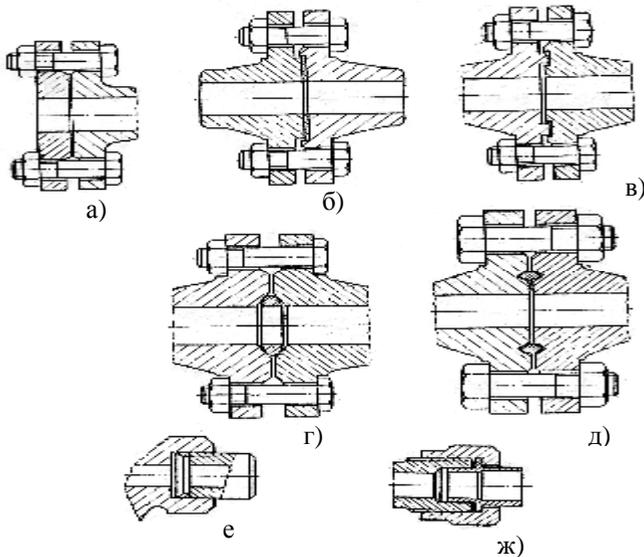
Основные типы присоединения арматуры к трубопроводу:
